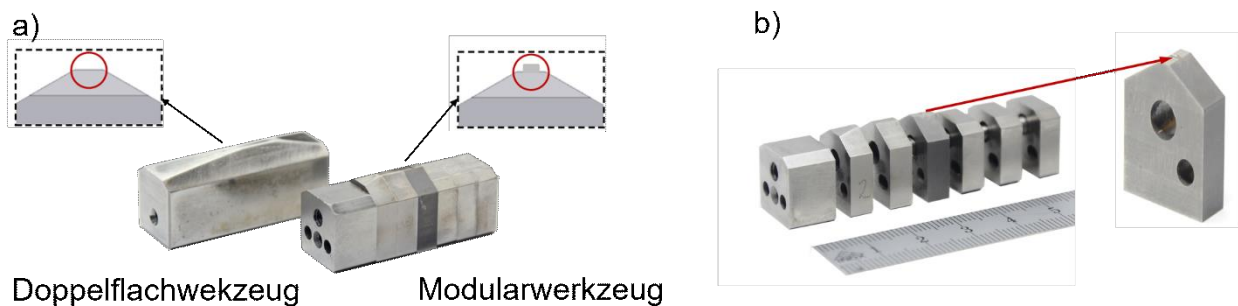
Rundknetwerkzeuge; a) Kombination von Werkzeugen für das Gewindekneten; b) Module für ein Modularwerkzeug nach [Ish20b].
